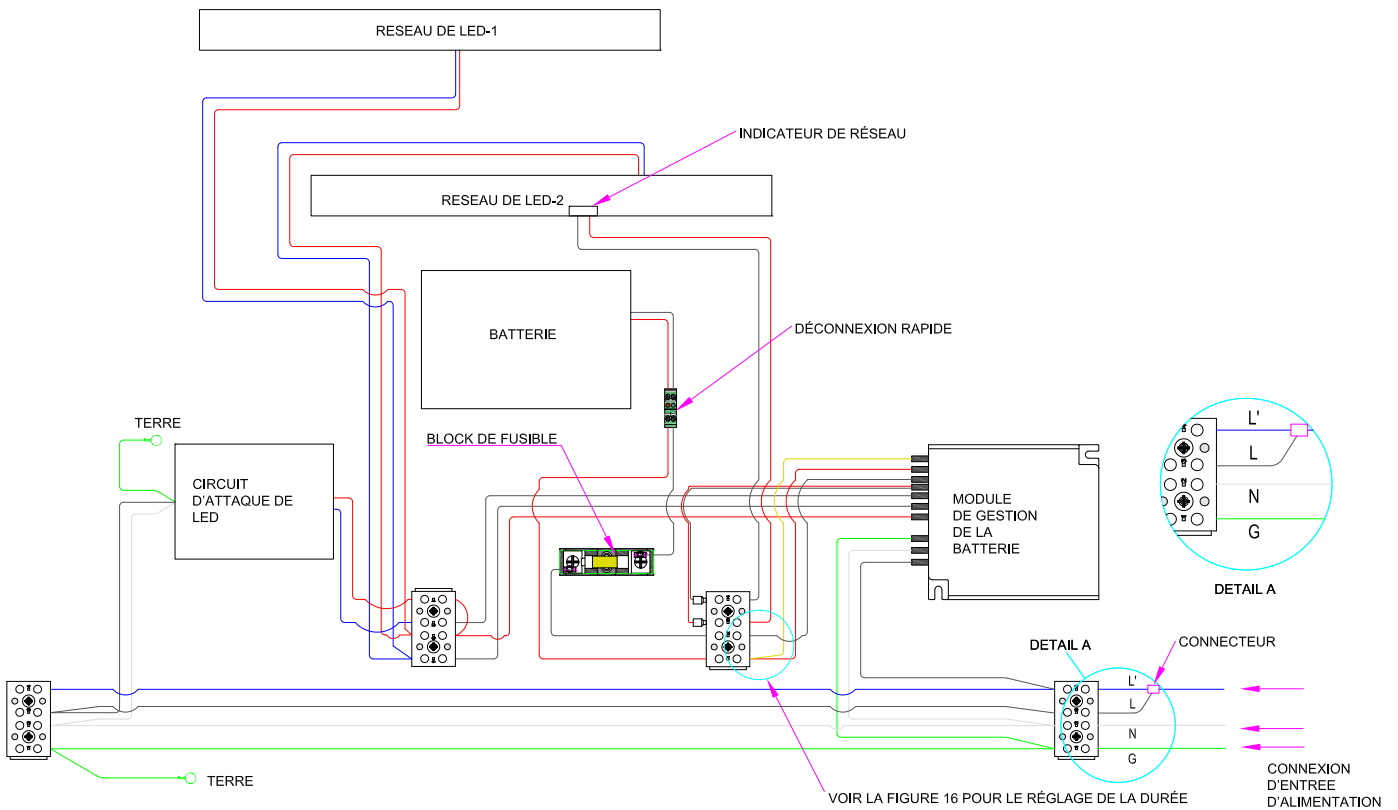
D: CABLAGE STANDARD, DISPOSITION DE CONNEXION A 3 FILS AVEC BORNES A VIS FIXES: 4 PIEDS
